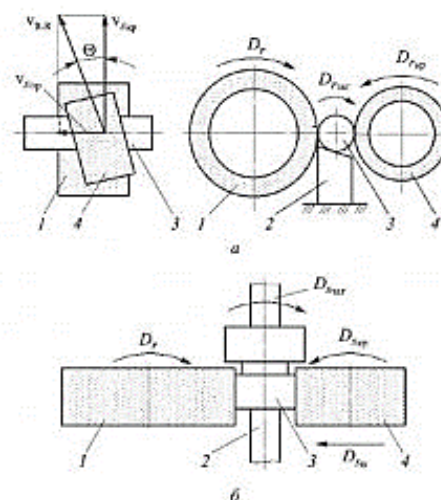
Схема обработки цилиндрической поверхности заготовок на бесцентрово-шлифовальных станках
